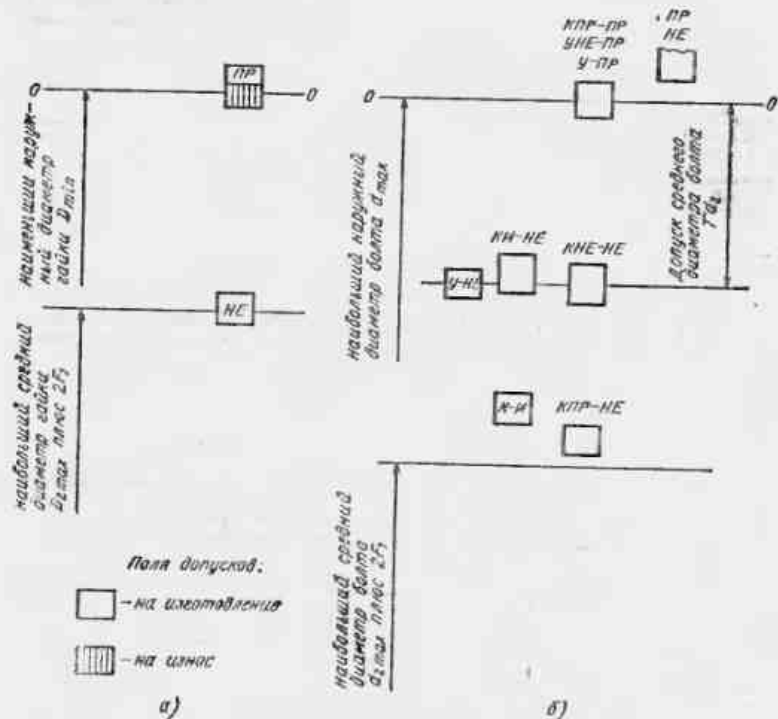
Схема расположения полей допусков наружного диаметра резьбы калибров для проверки:
